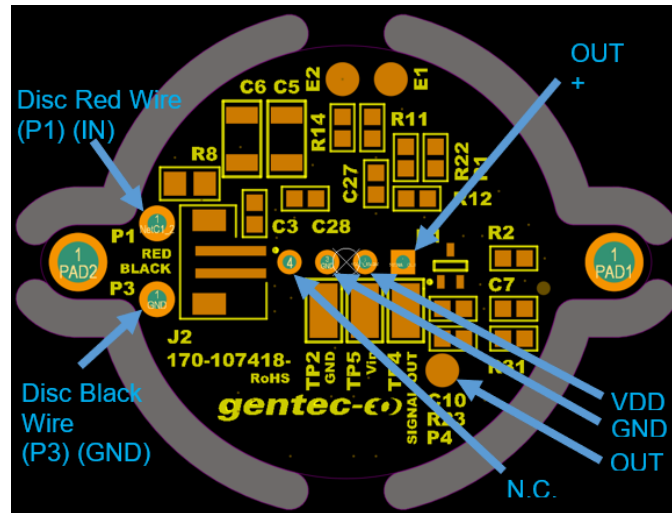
Vue du côté IC du PCB OEM 28V
